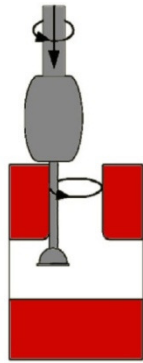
Das Werkzeug ins Zentrum der Bohrung führen.
